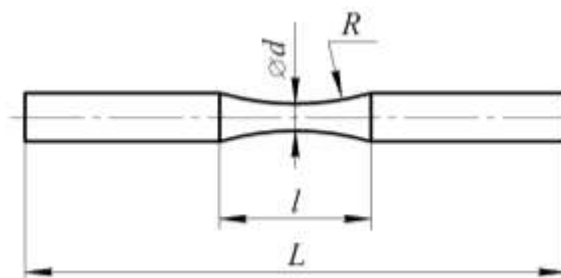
Эскиз образца корсетного типа для испытаний на усталость
